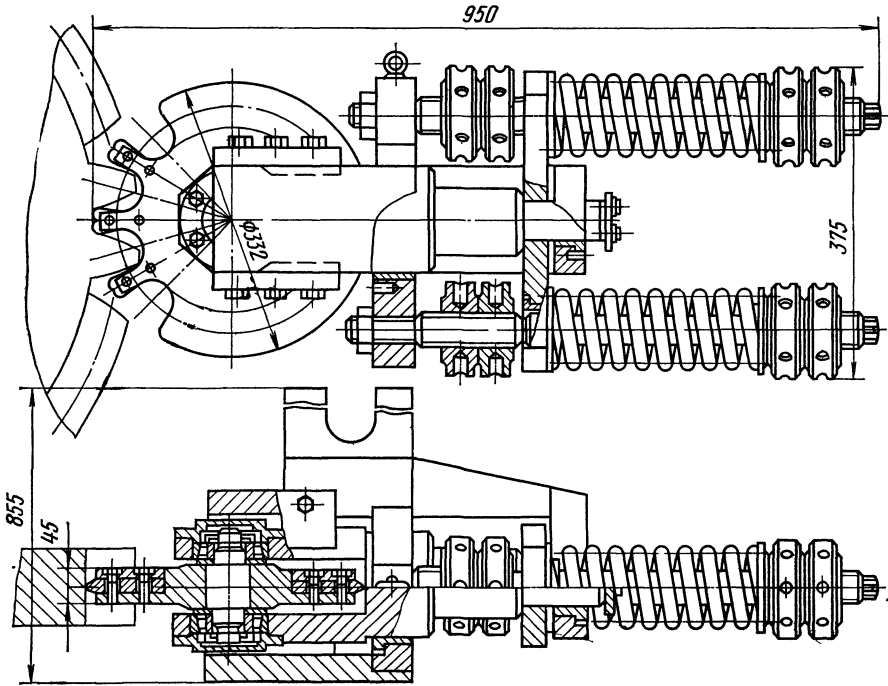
Устройство для поперечной обкатки зубчатых колес на токарном станке
